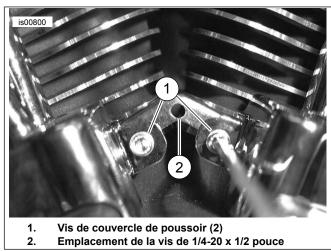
Ajustement de couvercle de poussoir et emplacement de la vis de couvercle de poussoir central
